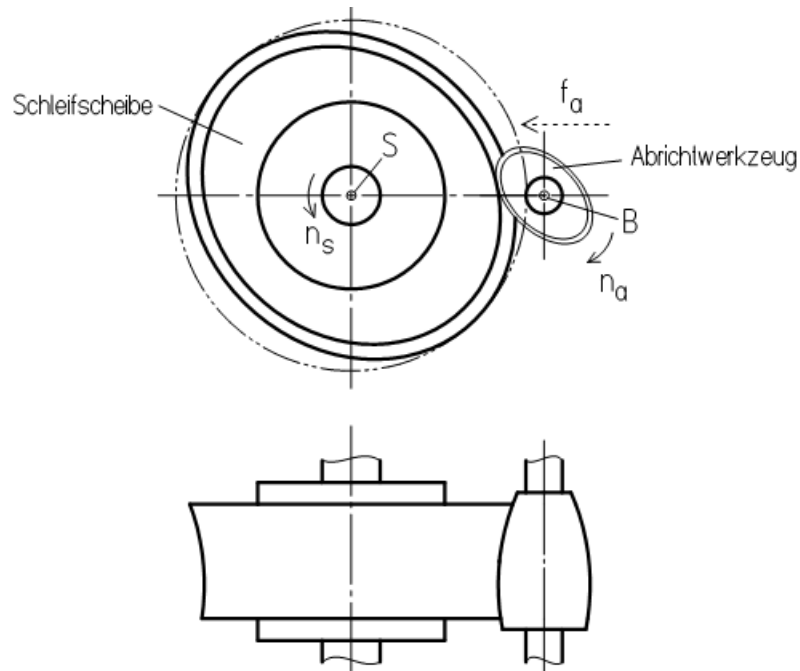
Unrundes und nicht zylindrisches Abrichten der Schleifscheibe mit einem der Werkstückform angepassten Abrichtwerkzeug [ABL12a]
